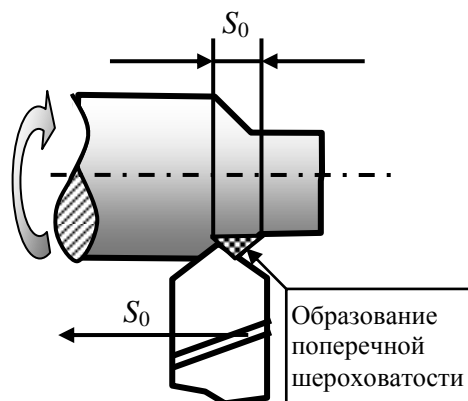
Эскиз токарной обработки,  $S_0$ – подача на один оборот вращения заготовки.
